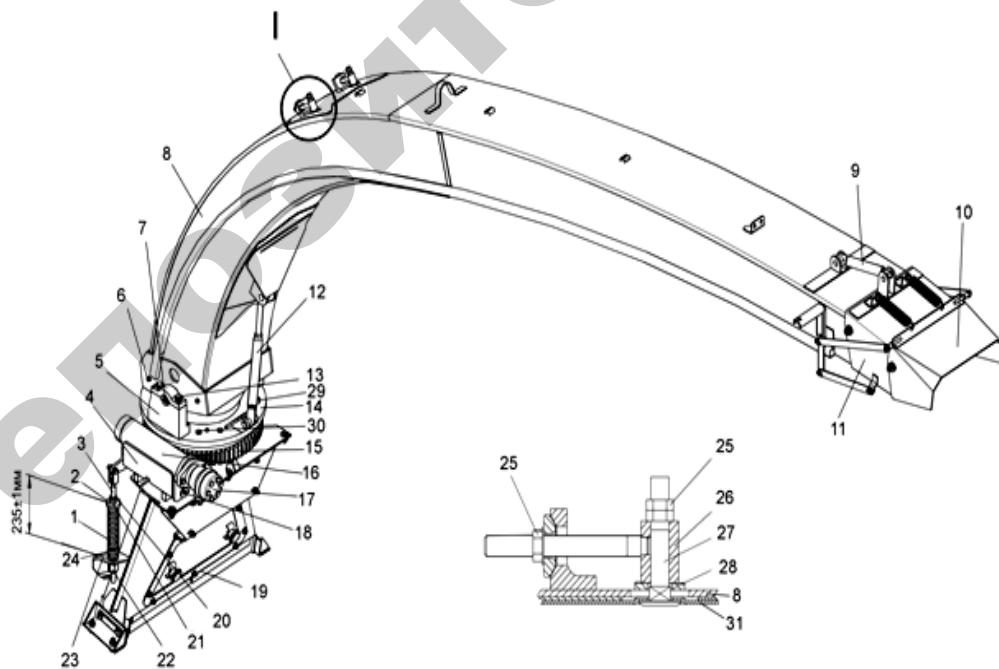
Основание силосопровода с механизмом поворота и силосопровод:
